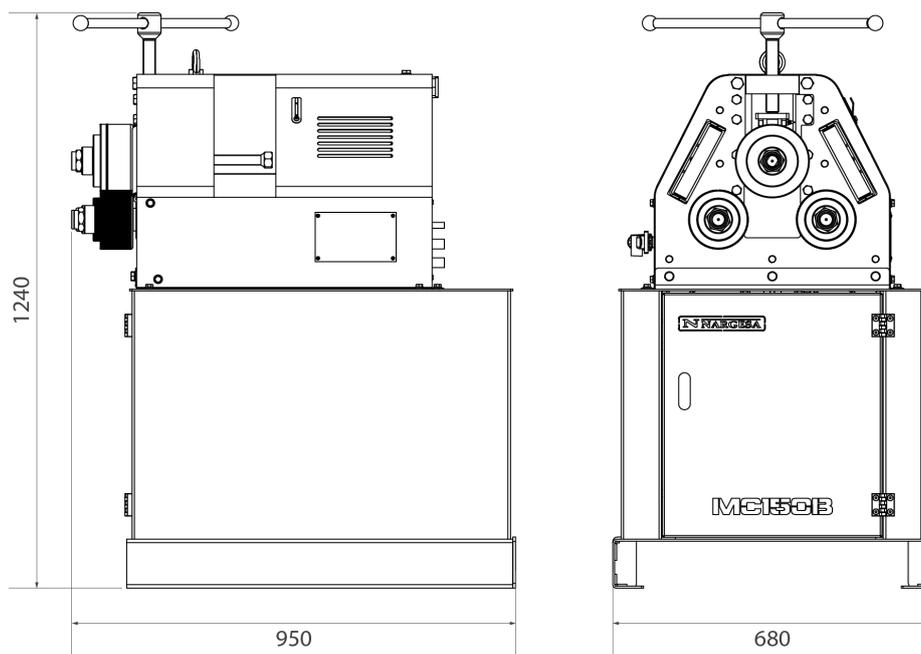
Dimensions extérieures de la cintreuse MC150B
